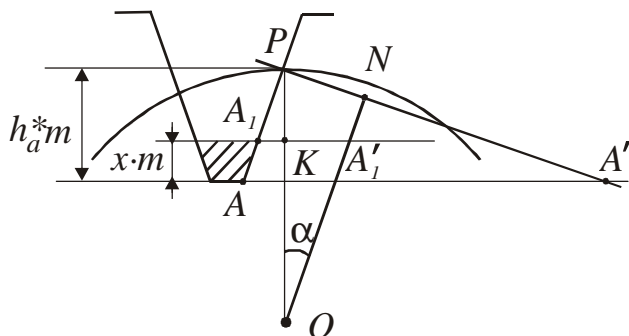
Предельный случай расположения инструментальной рейки и заготовки для нарезания зубьев без подрезания
